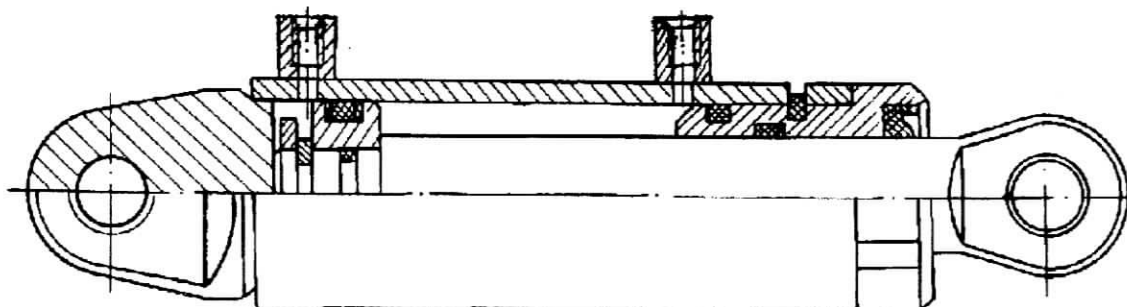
Гидроцилиндр ГА-93.000-06: наклона козырька силосопровода - 1 шт
